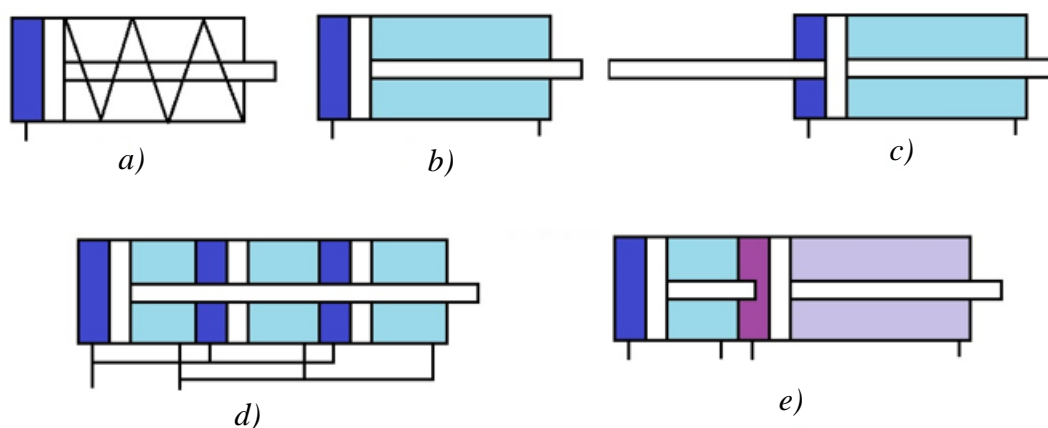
Přímocaré motory dle normy ISO 15552
